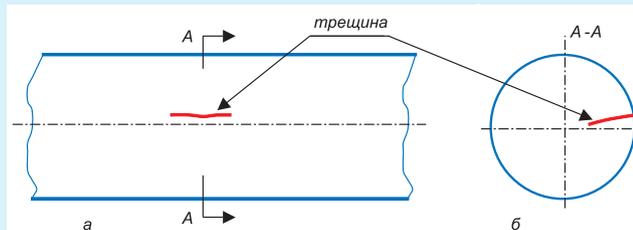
Трещина, выходящая на поверхность цилиндрической детали: а – вид трещины на цилиндрической поверхности; б – вид трещины в сечении А-А
